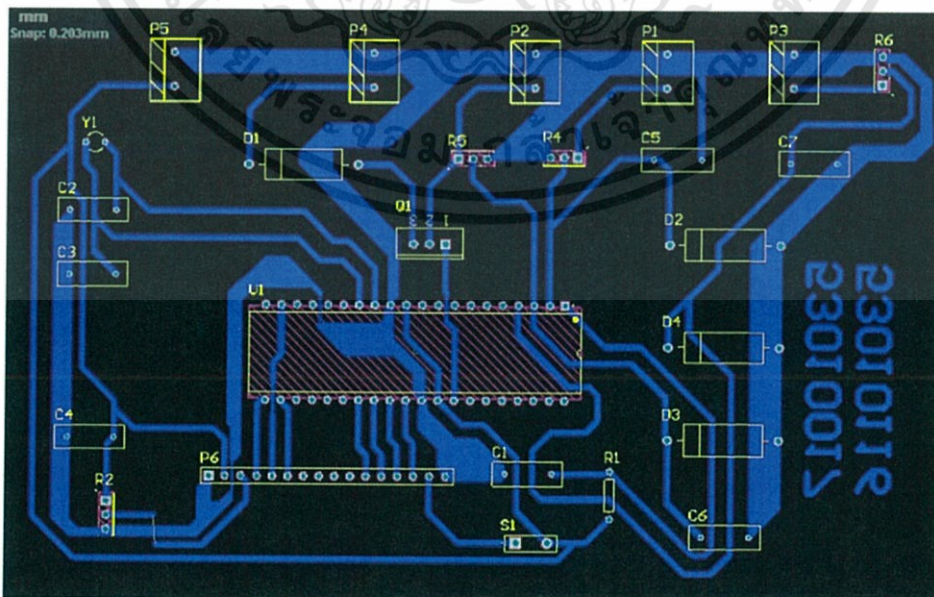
PCB (Print Circuit Board) ของวงจรควบคุมแรงดันขาออกให้คงที่
